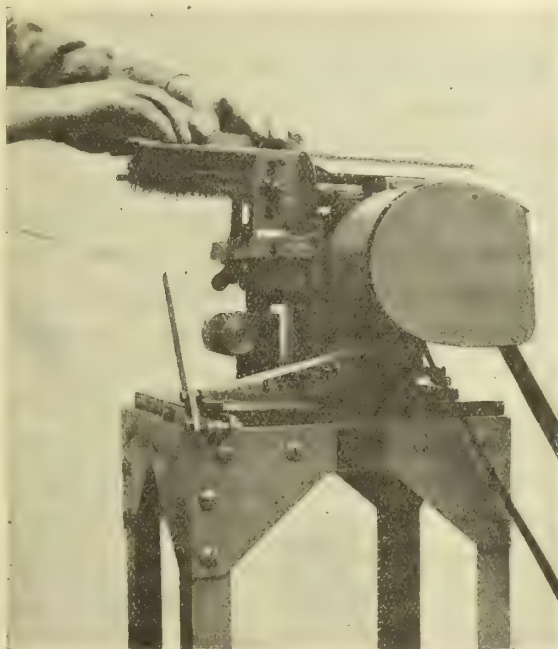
Fig. F. — Vue perspective de la machine de M. H. Vollet. La machine en marche : vue d'ensemble.
